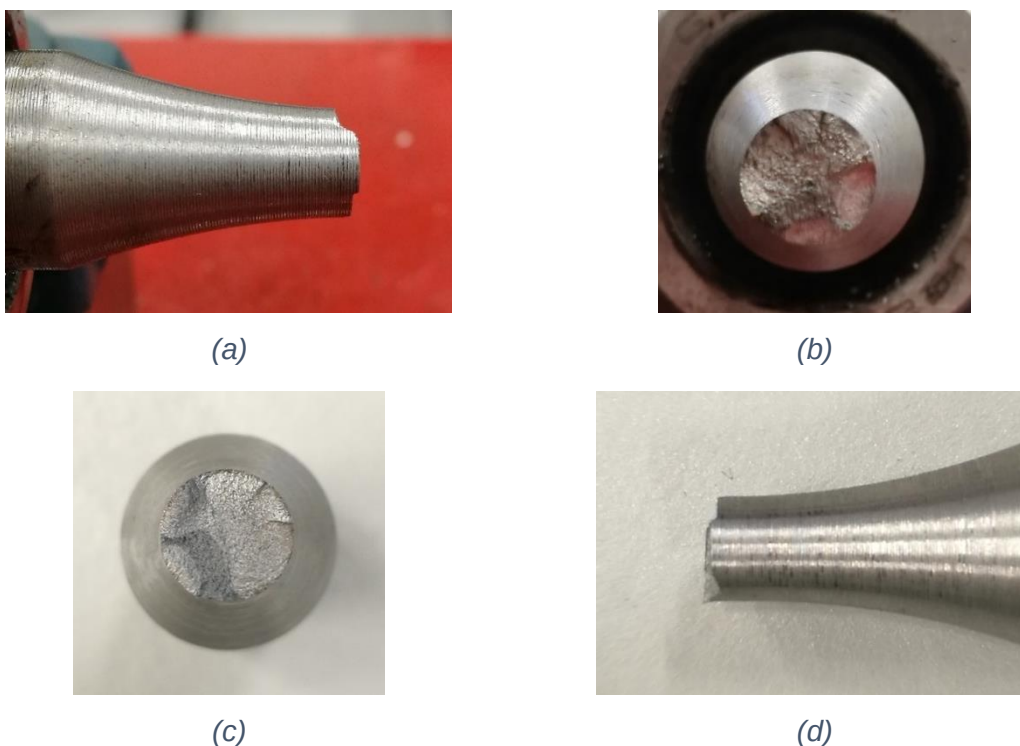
Fisura de la probeta de planos paralelos con entalla a 24 kg. (a) Vista lateral del extremo fijo al eje del motor. (b) Vista frontal del extremo fijo al eje del motor. (c) Vista frontal del extremo en voladizo. (d) Vista lateral del extremo en voladizo.
